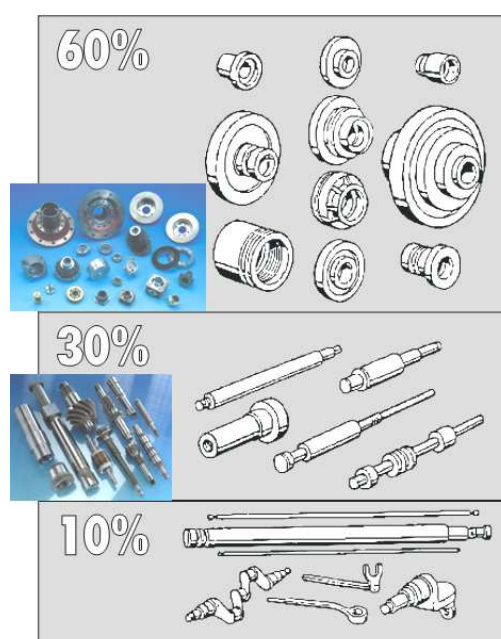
Famílias de peças cilíndricas usinadas em tornos (EMAG MASCHINENFABRIK, 2009).
